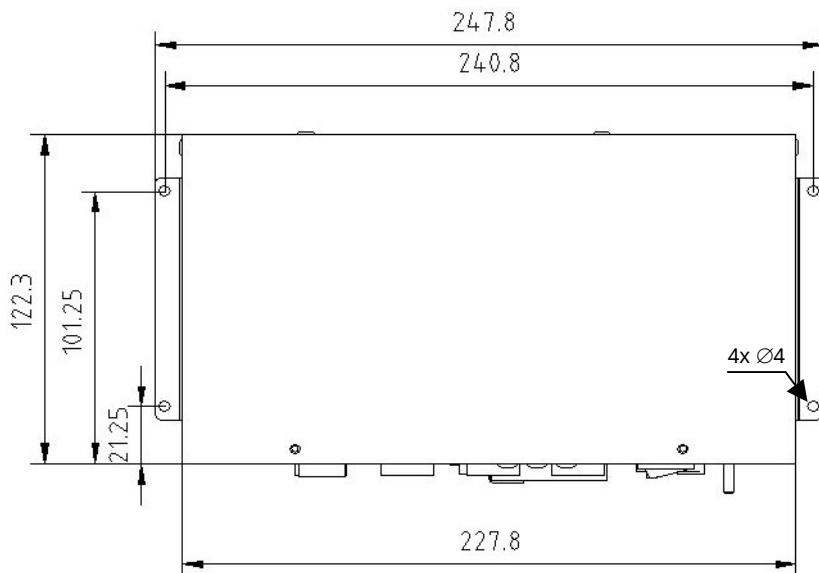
Lochbild für die Wandmontage der JReX-IBOX
